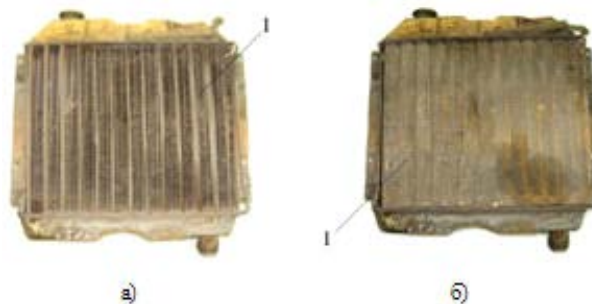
Радиатор с трубчато-ленточным остовом, снабженный жалюзи:
